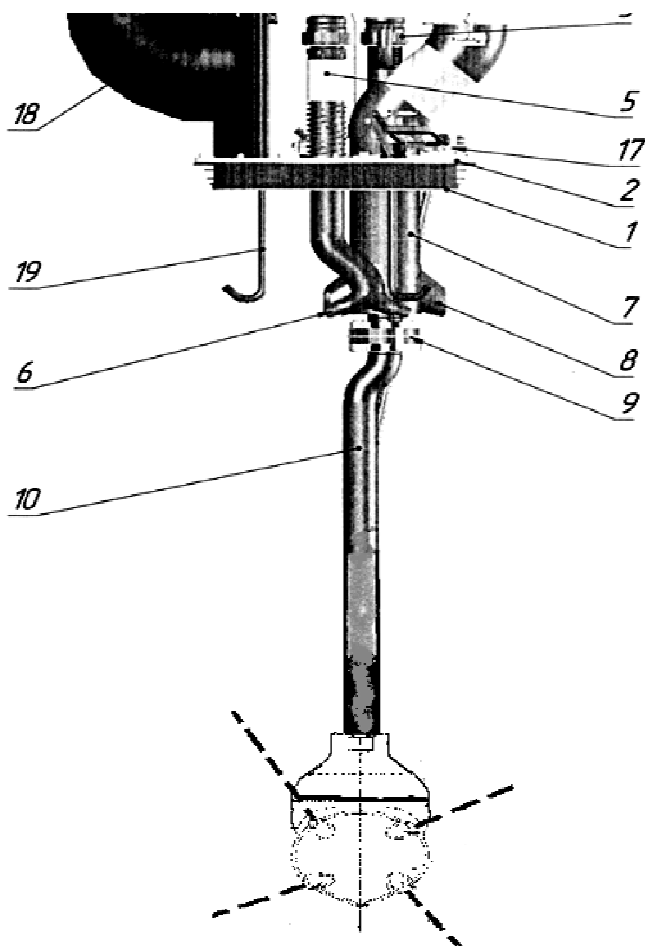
Мийна установка з ротаційною форсункою
